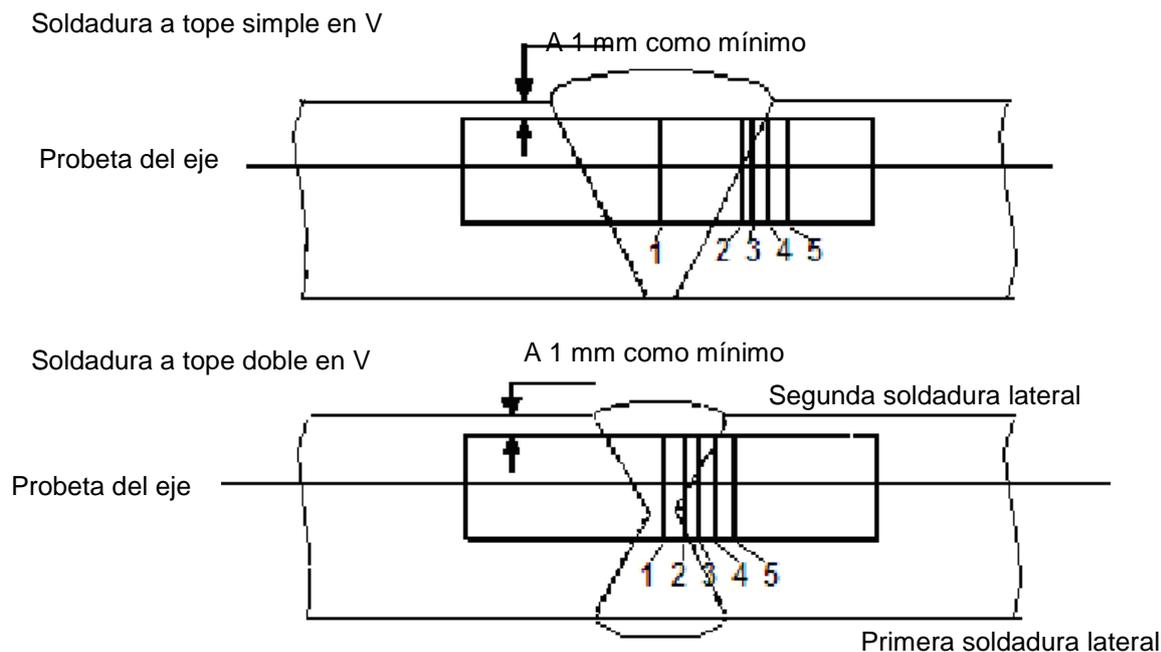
Orientación de la probeta de la prueba de soldadura
